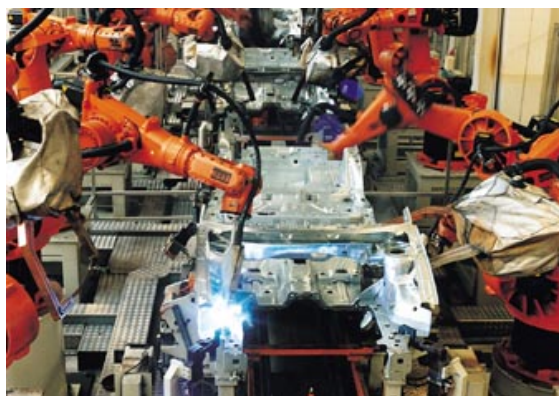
Roboter beim Punktschweißen
